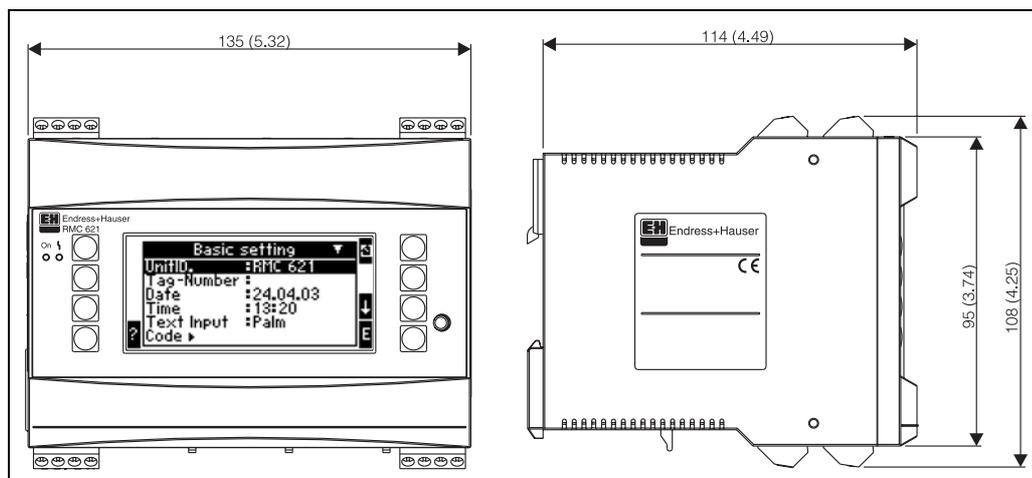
Корпус для монтажа на шину DIN по EN 50 022-35; размеры даны в мм (дюймах)
